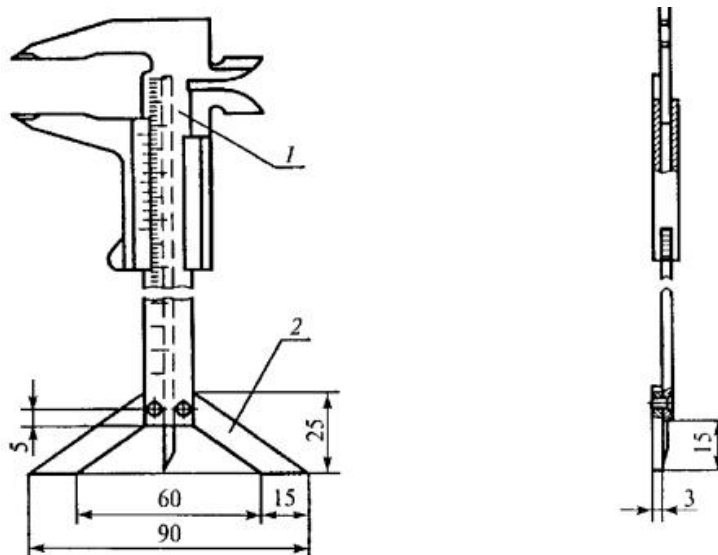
Штангенциркуль типа ШЦ- 1 с опорой
